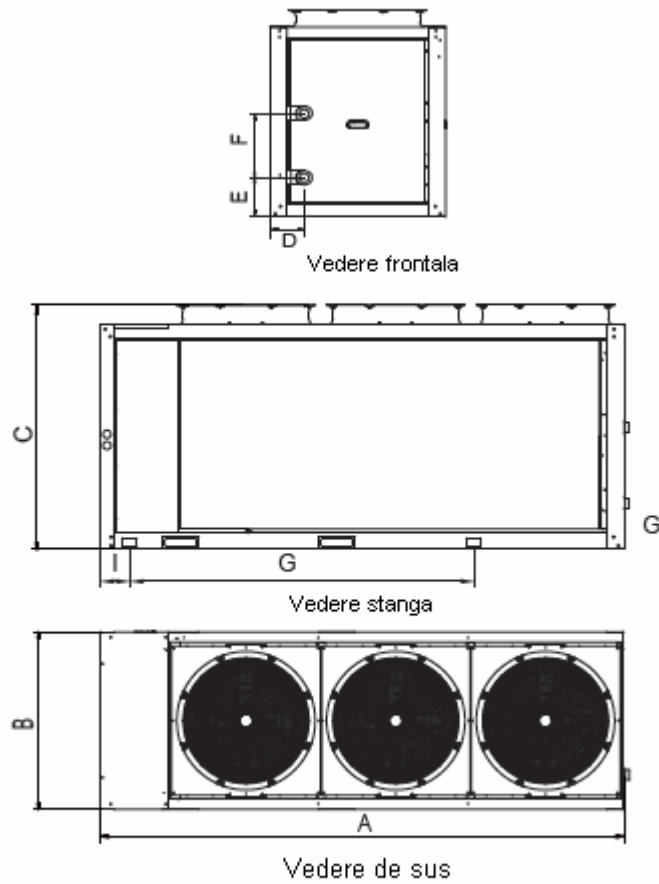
Desene dimensionale MC-SU90-RN1L
